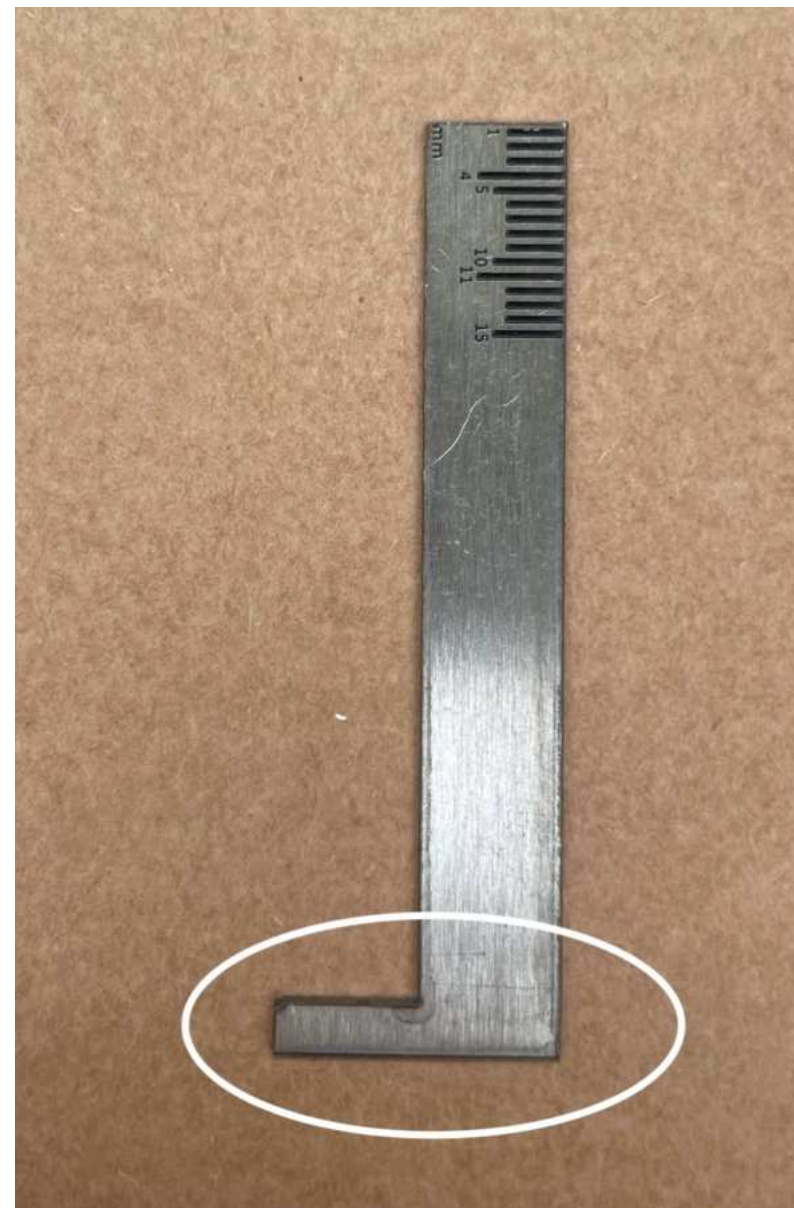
Messwerkzeug für den Abstand zwischen Platte und Taste
